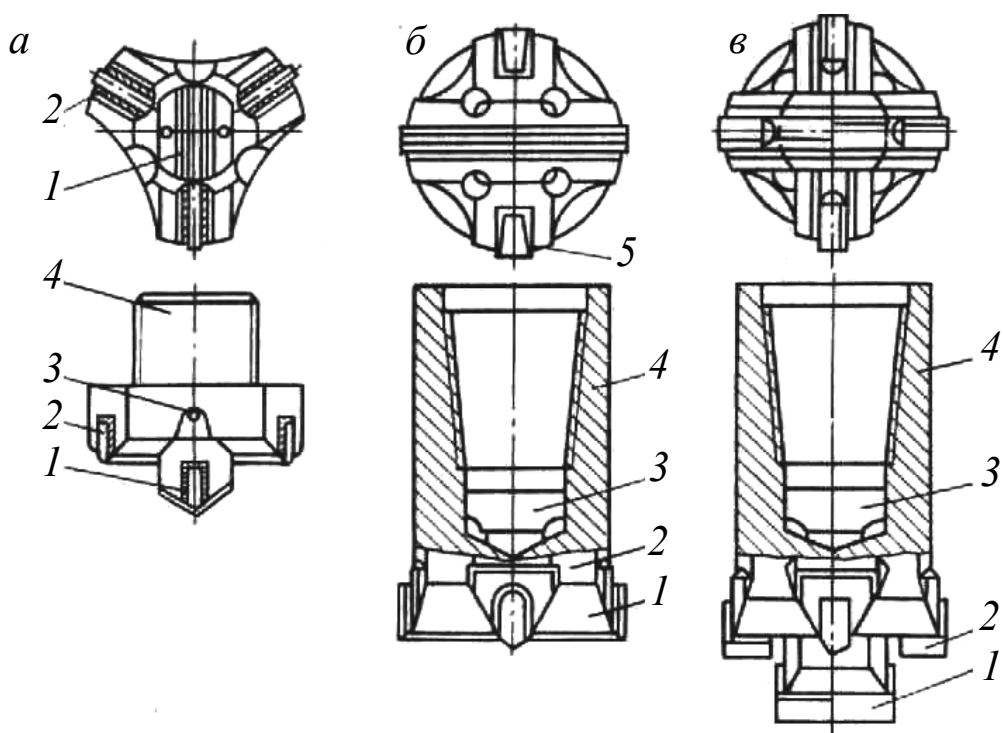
Конструкции долот для гидроударников: 1 – центральная вставка; 2 – боковые вставки; 3 – циркуляционные каналы; 4 – корпус; 5 – калибрующие вставки
